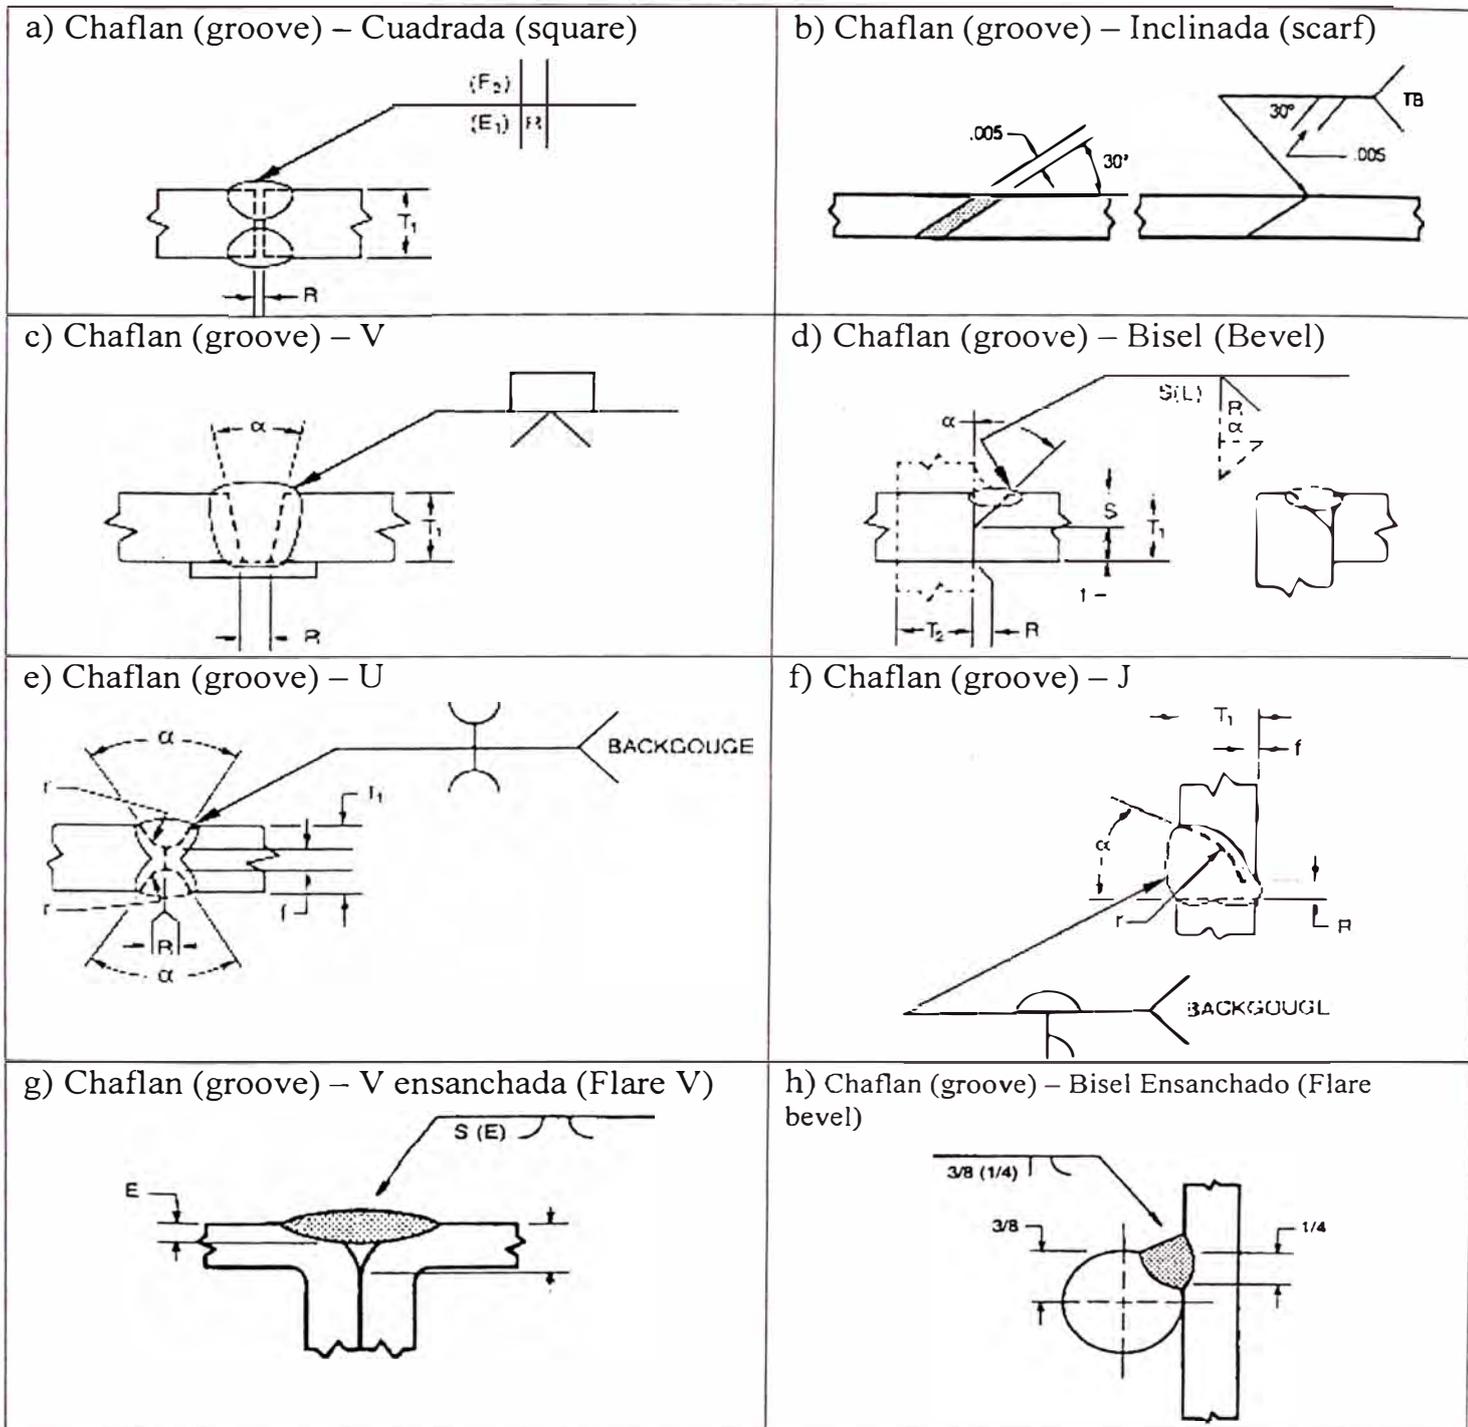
Tipos de Soldadura (Ver bibliografía N°2)
